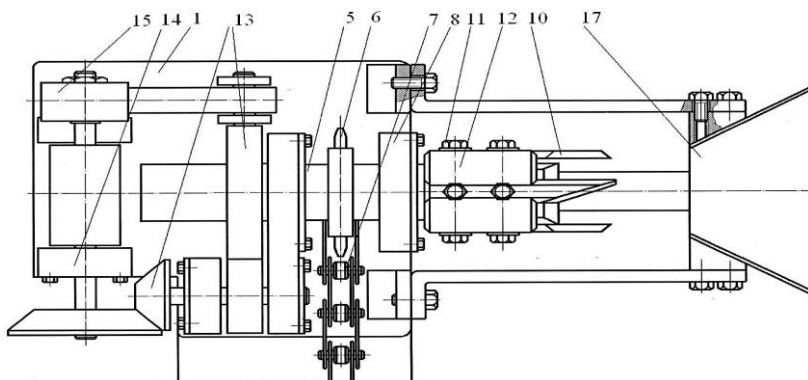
Устройство для заготовки хвойной лапки (вид сверху)
